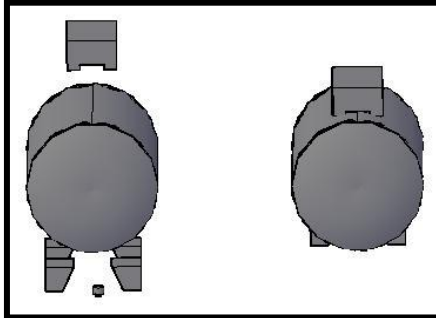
Desenho tridimensional do processo de soldagem das peças: pé, base e conexão.
